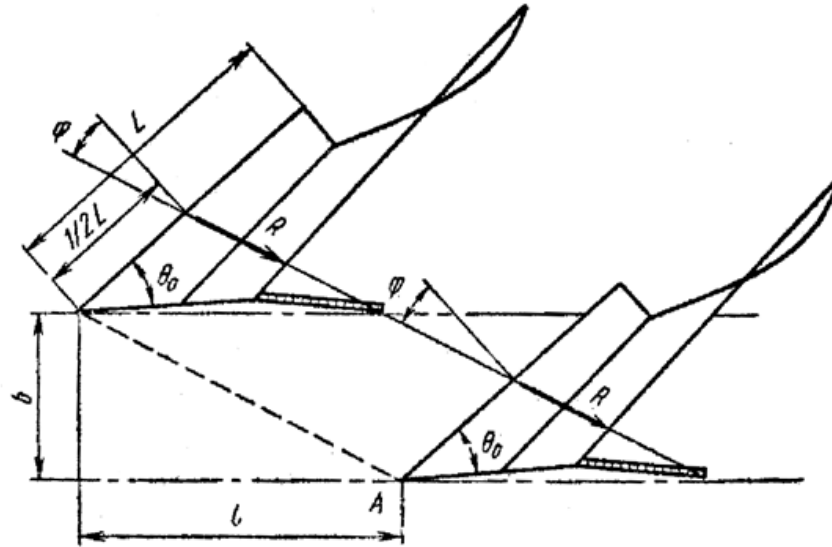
Схема розстановки корпусів у повздовжньому напрямку
